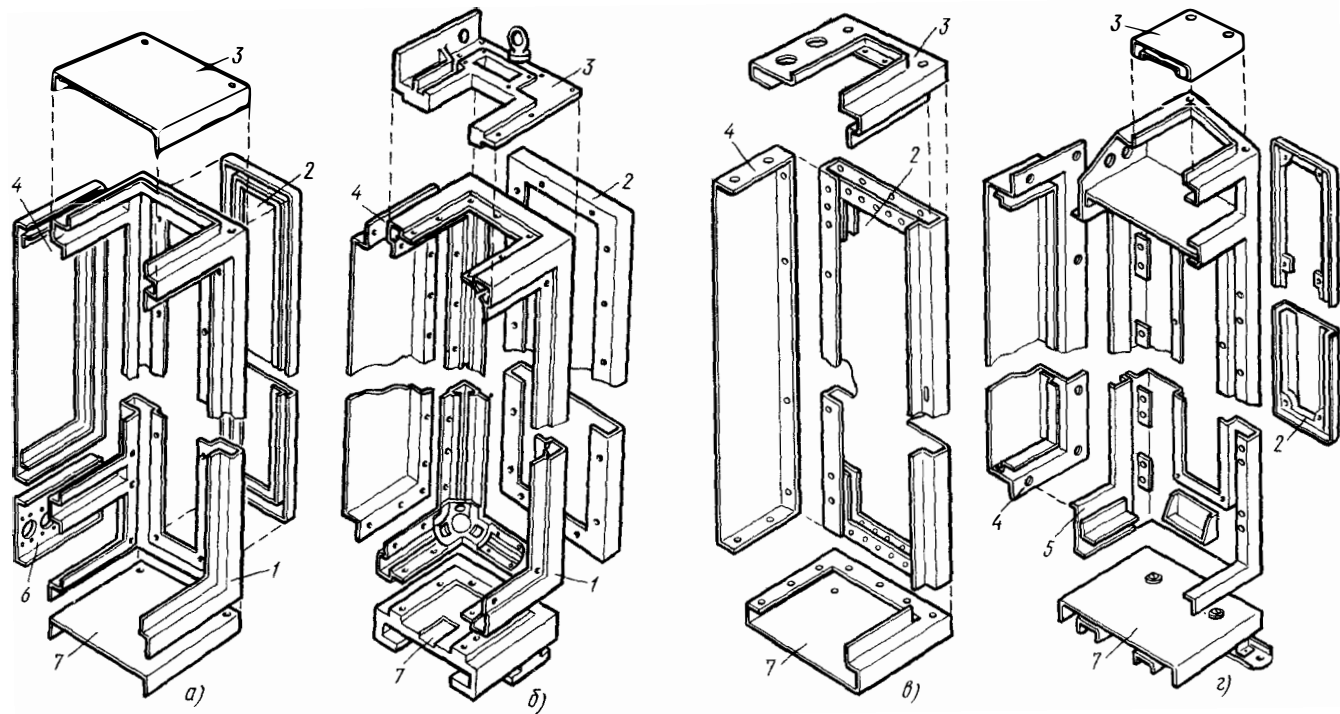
Конструкции стоек мини-ЭВМ:
